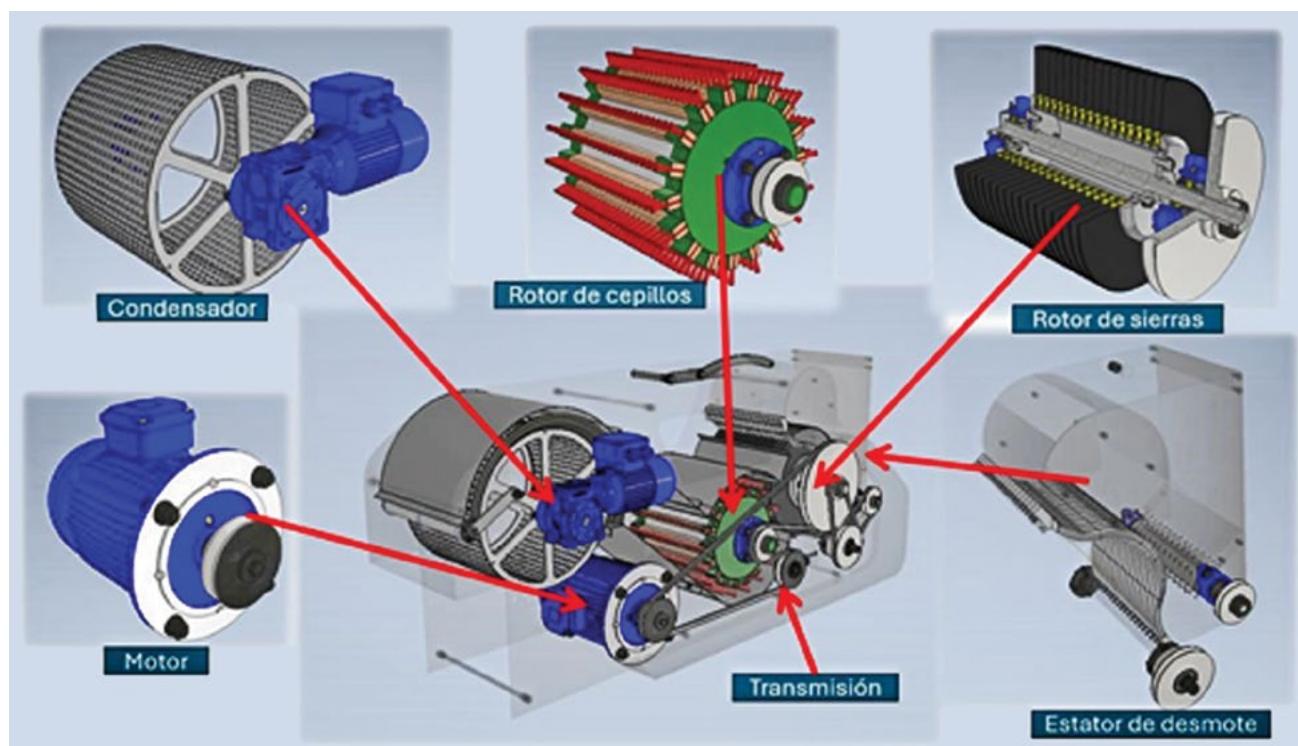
Principales componentes de la máquina diseñada. Se muestra el diseño tridimensional (3D) realizado en computadora, indicando las principales partes que lo componen.
